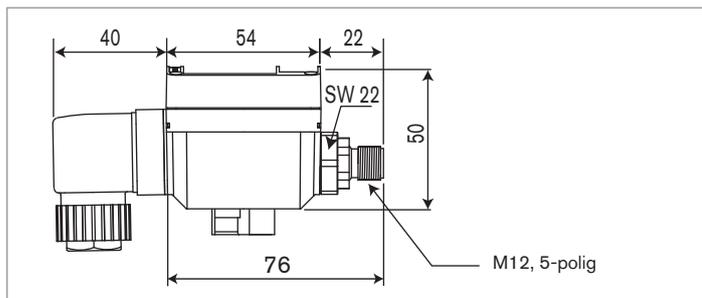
Abmessungen [mm] des Elektronikmoduls SE32 mit 5-poligem M12-Gerätestecker
